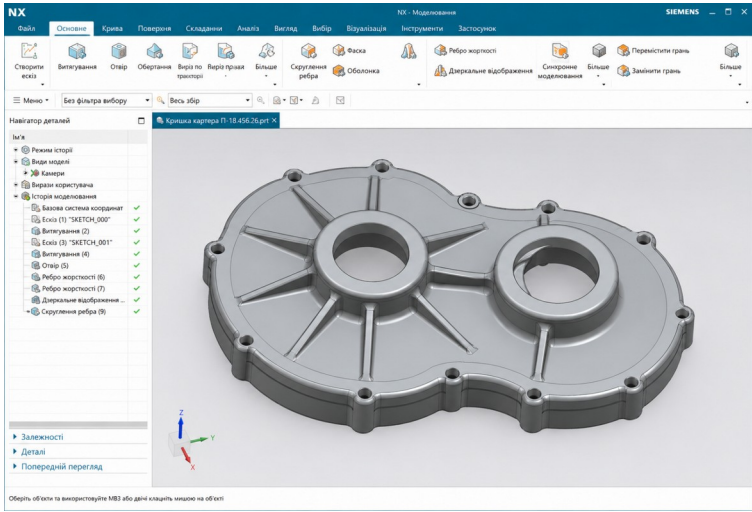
3D-модель деталі «Кришка картера П-18.456.26»
